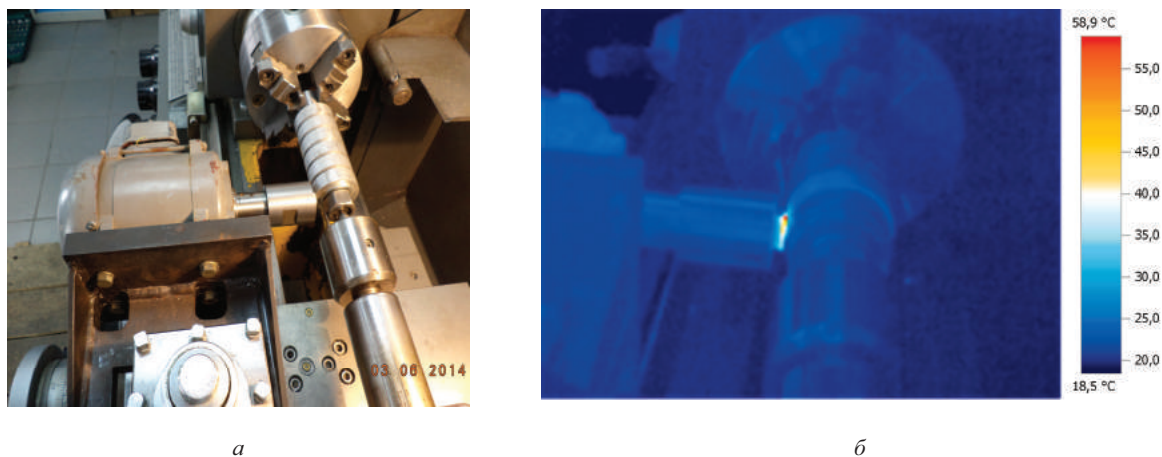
Инструментальный модуль на базе токарно-винторезного станка ИЖ250 ИТВМ.Ф1:
